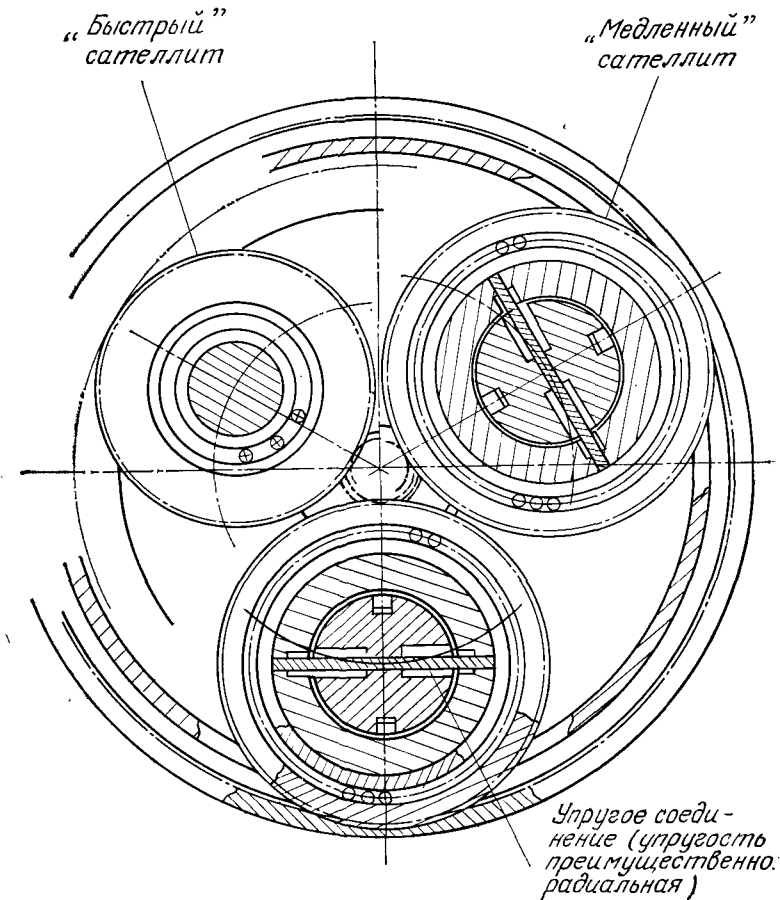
б. Несогласованный эпициклический редуктор (дополнительный вид).
